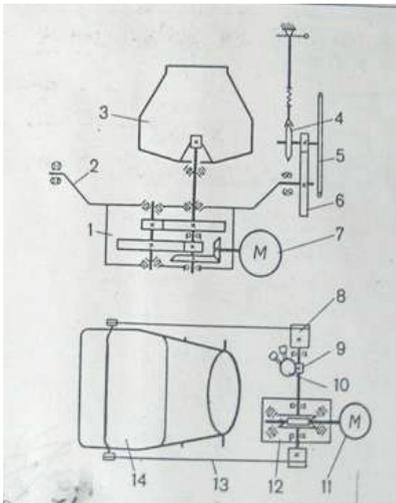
Кинематическая схема смесителя СБ-30Г: 1 – редуктор привода смесительного барабана; 2 – траверса; 3 – смесительный барабан; 4 – тормоз; 5 – штурвал механизма опрокидывания; 6 – одноступенчатый редуктор механизма опрокидывания; 7 – электродвигатель привода смесительного барабана; 8 – подъемный барабан; 9, 10 – концевые выключатели; 11 – электродвигатель механизма подъема ковша; 12 – червячный редуктор; 13 – канат подъемного механизма; 14 – ковши
